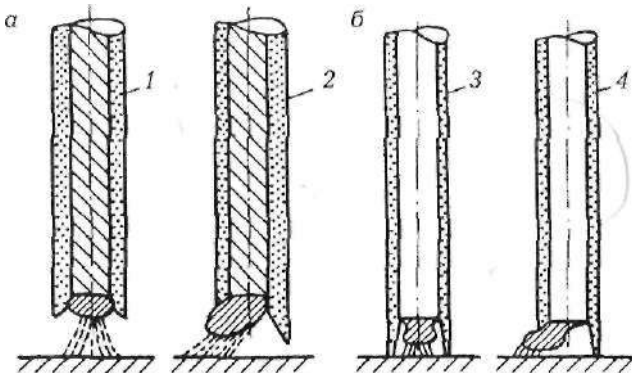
Образование козырька при сварке электродами:
